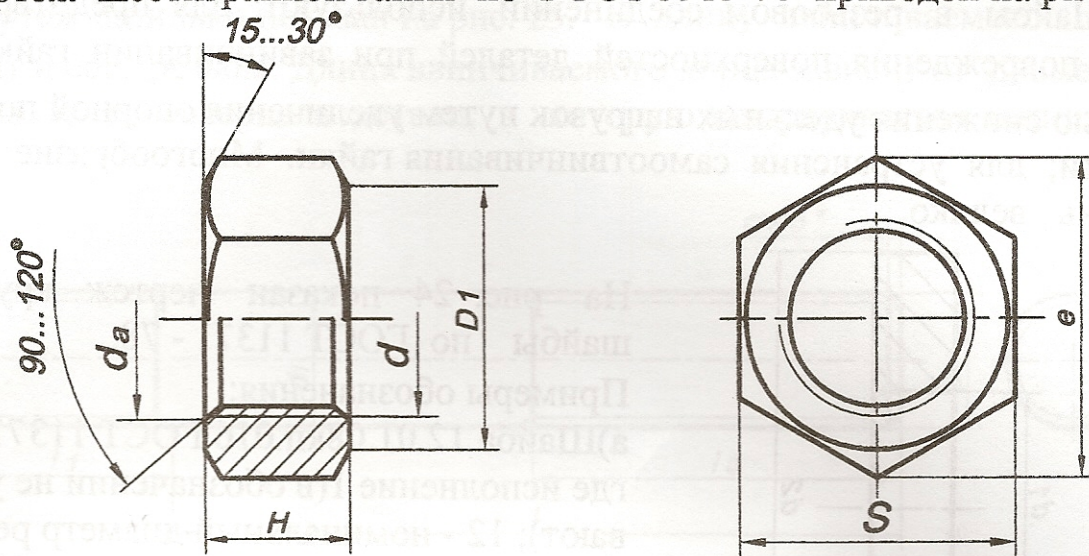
Чертеж гайки: d -номинальный диаметр резьбы; S - размер под "ключ"; e - диаметр описанной окружности; d_a ($1.05d$)- диаметр фаски резьбы; D ($0.9S$) - диаметр фаски; H - высота гайки
